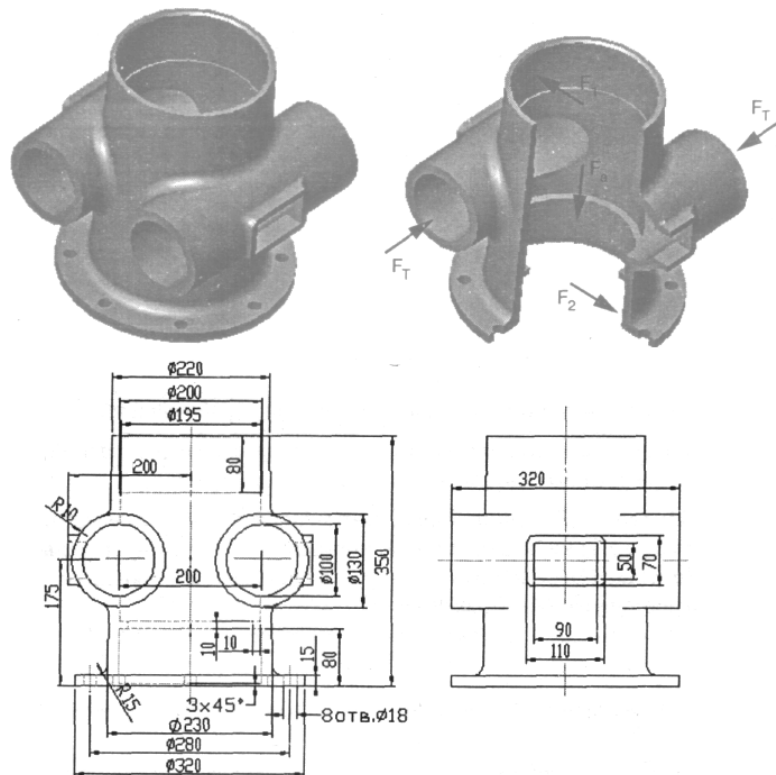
Внешний вид корпуса поворотного механизма манипулятора с указанием приложенных нагрузок и его геометрические параметры
